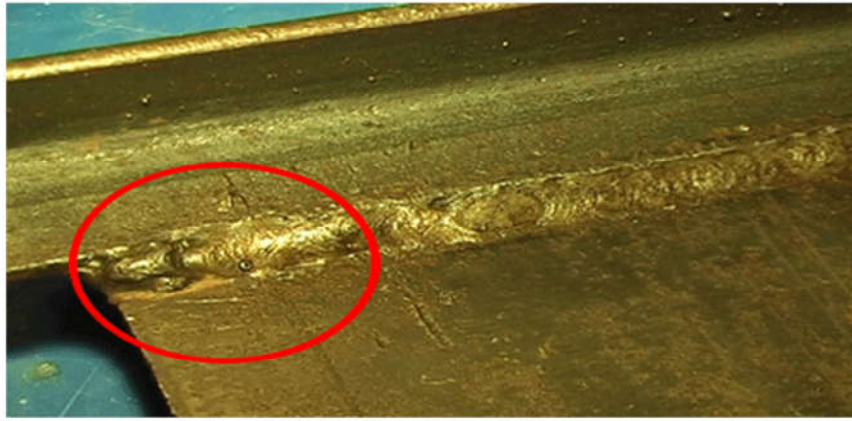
Дефект зварного шва (непровар)
